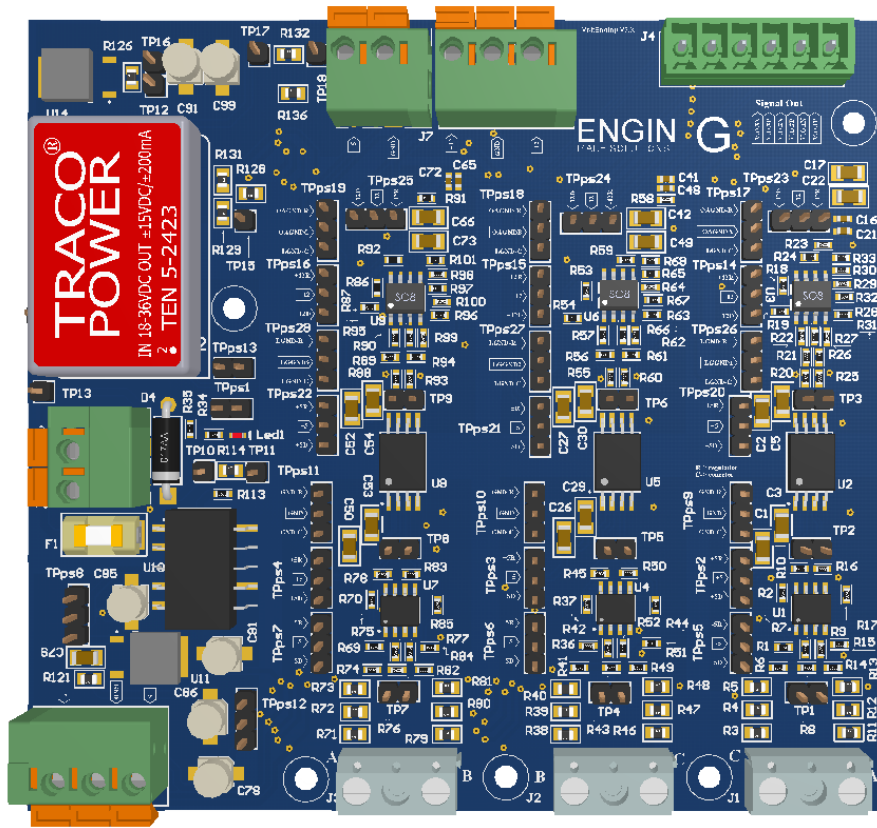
Desenho PCB da placa SMTGI, camada superior.
